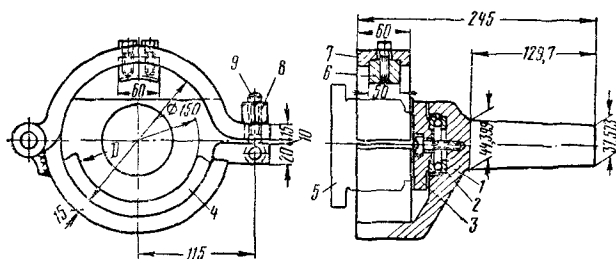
Приспособление для токарной обработки коллекторов тяговых двигателей:
